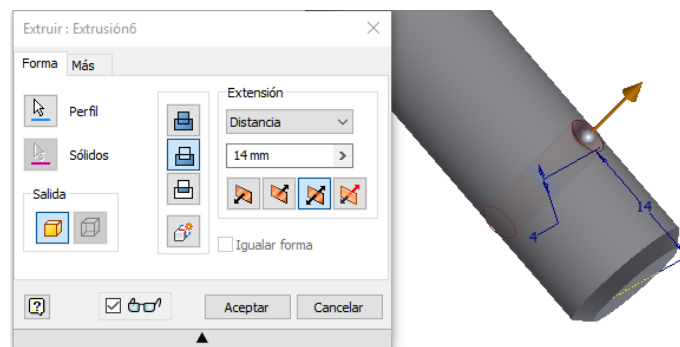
Agujereado en el extremo del eje mediante extrusión.
